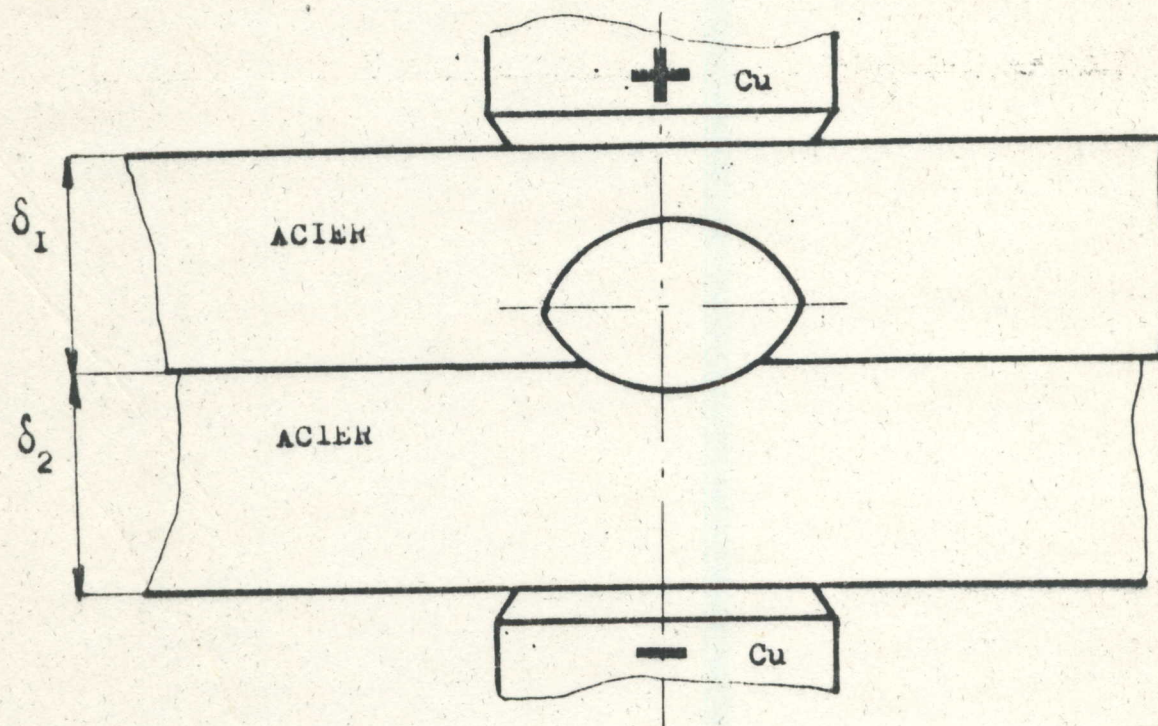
Soudage en utilisant un courant unipolaire.
